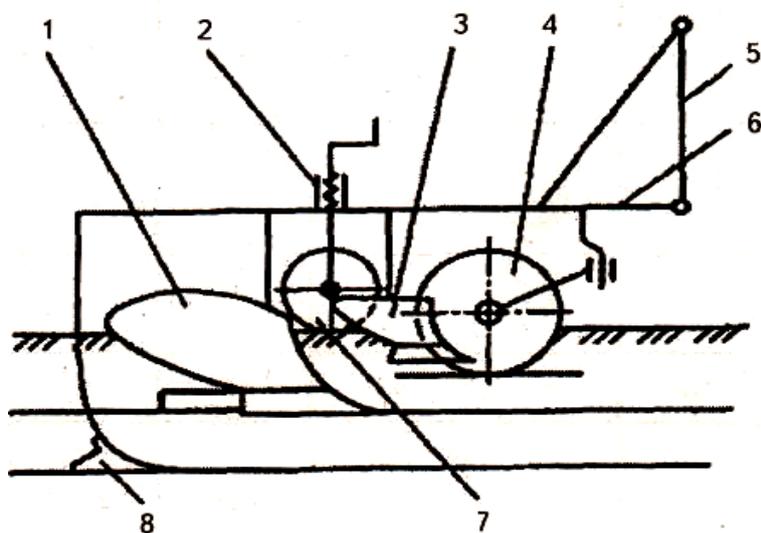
Общее устройство однокорпусного навесного плуга: 1 – корпус плуга; 2 – винтовой механизм опорного колеса; 3 – предплужник; 4 – нож; 5 – навесное устройство; 6 – рама плуга; 7 – опорное колесо; 8 – почвоуглубитель
